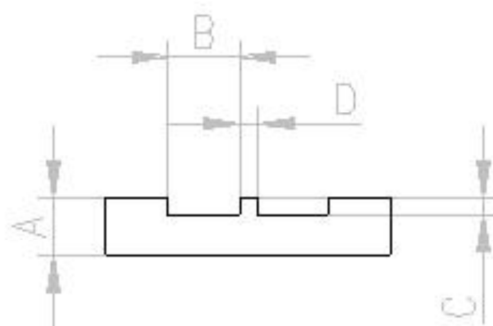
Plaques composant un module élémentaire d'un ETR (source Institut de Soudure IS).
